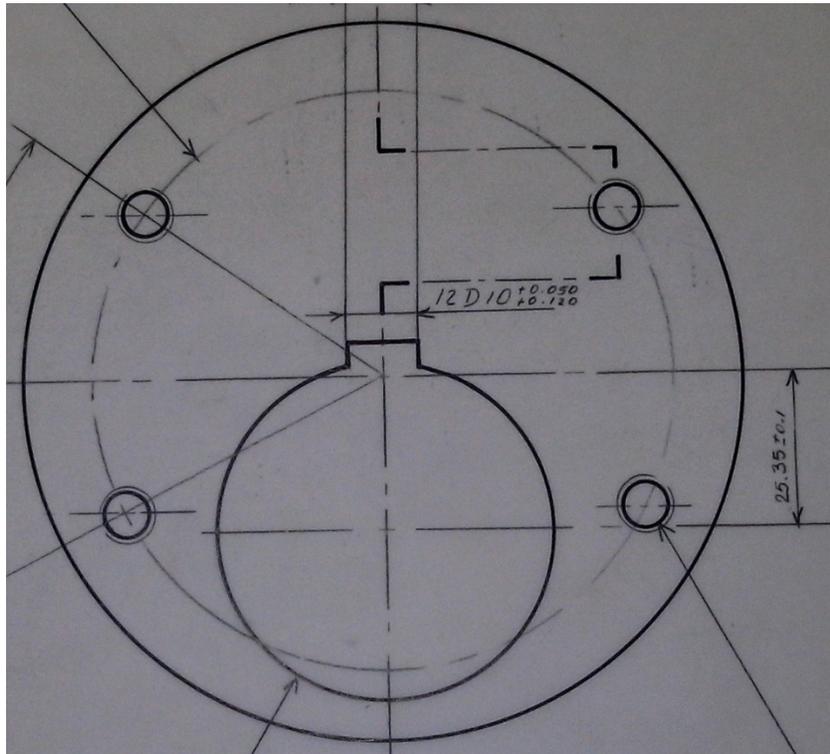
Altura de la pieza A3-004 Excéntrica.
